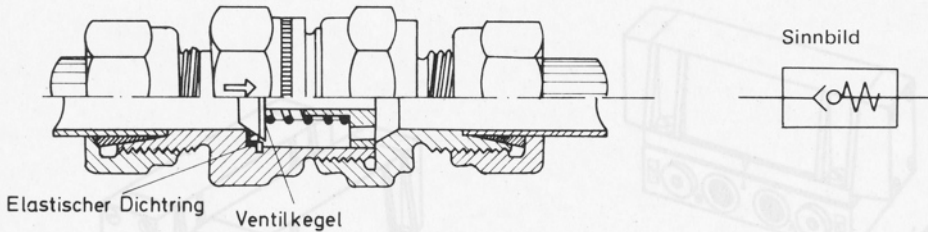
Federbelastetes Rückschlagventil (Ermeto)
